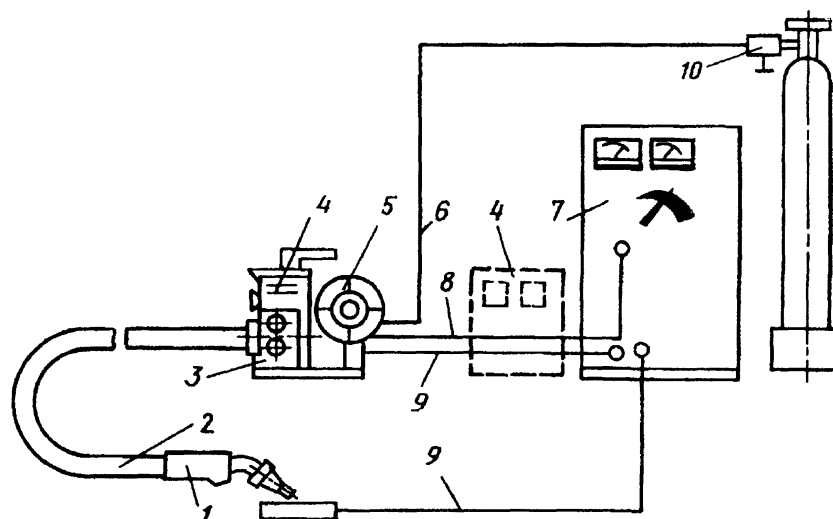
Напівавтомат зварювальний «КРИСТАЛ ПДГО-570-4К»
